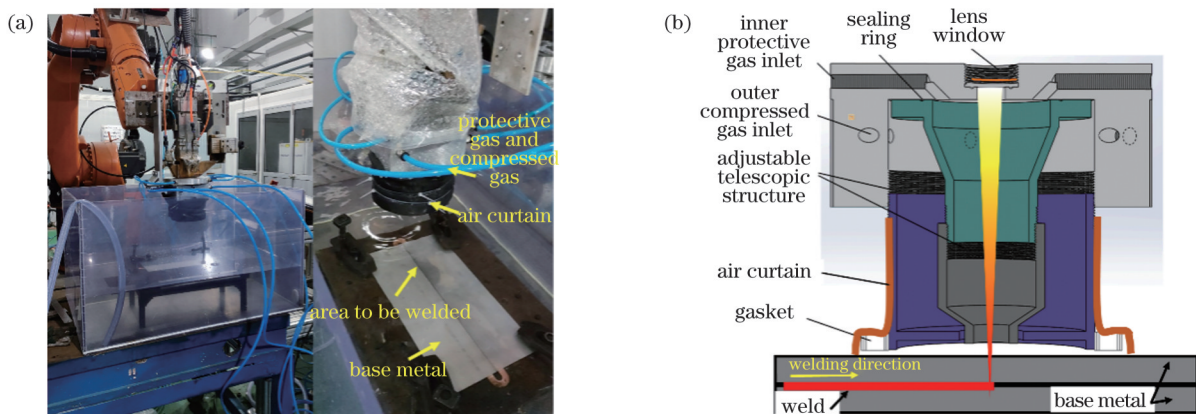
焊接试验装置及焊接过程示意图。(a)焊接试验装置照片;(b)局部干法装置及焊接过程示意图
